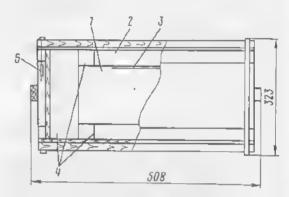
Схема упаковки прибора; 1 — укладочный ящик; 2 — влагозащитная бумага; 3 — полиэтиленовый чехол; 4 — полушка (гофрированный картон); 5 — пломба
